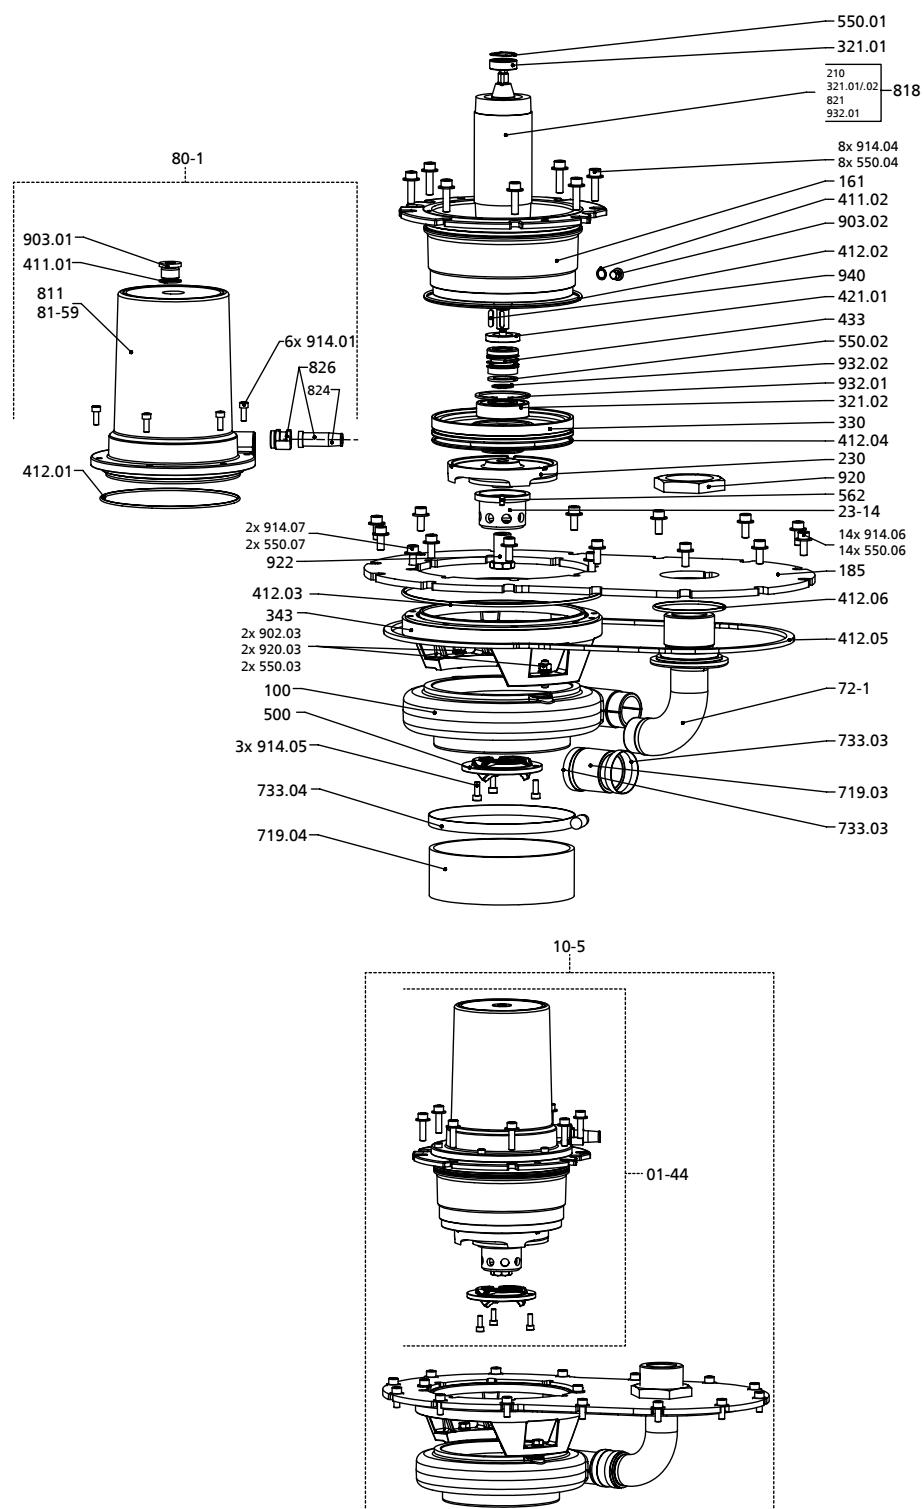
Explosionsdarstellung US100, UZS150 - Laufteil
